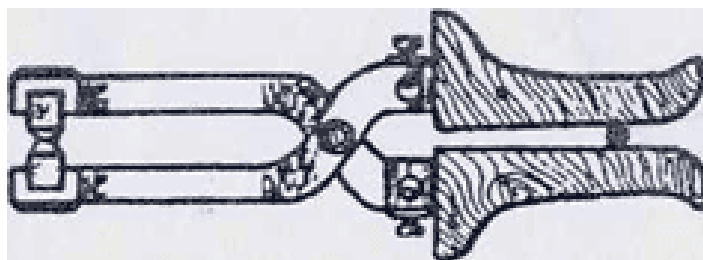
Клещи Бенардоса для контактной сварки
